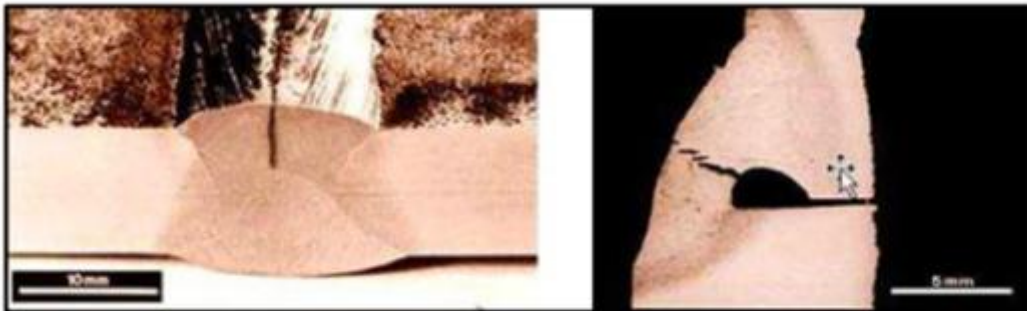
Fissuration à chaud d'un joint soudé (Réf. [R16])
